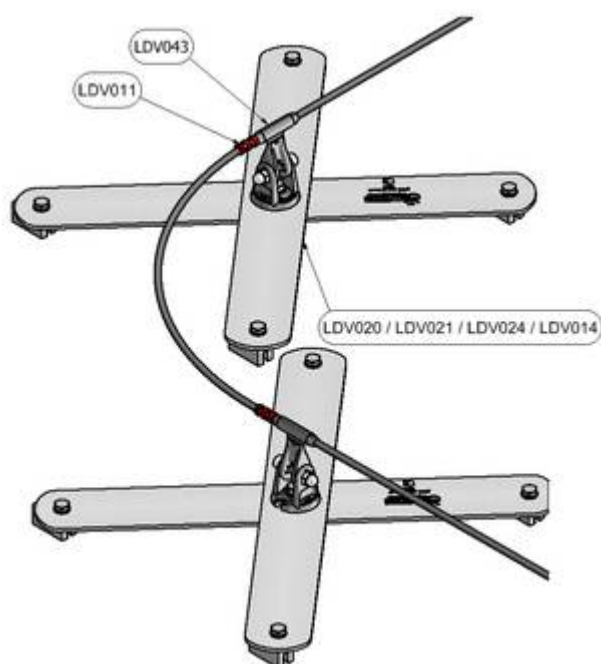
Montage ancrs intermédiaires avec bagues à sertir dans virage sur toiture à joints debout
